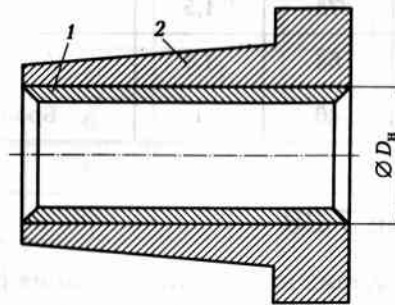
Сборочный чертеж соединения деталей к заданию 7.27
